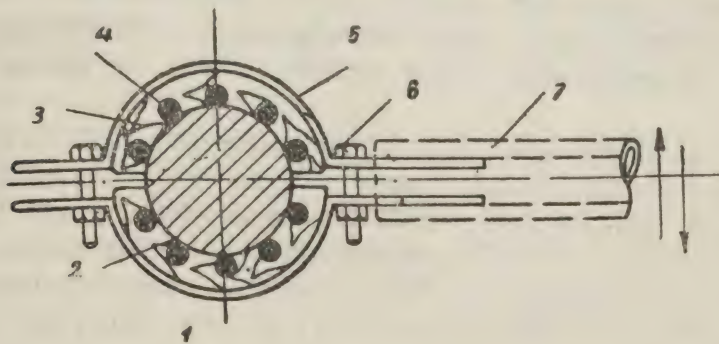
Колодка для ручной выборки царапин, рисунок и эллипсоидности шеек вала:
